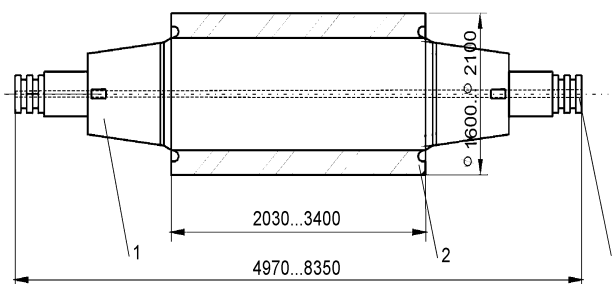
Базовая конструктивная схема составного крупногабаритного прокатного валька: 1- ось валька; 2 – бандаж (штулка); 3 – пробка оси
